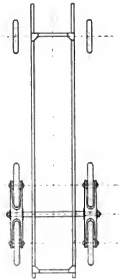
Chassis mit einer Wagenachse mit 4 Rädern.
